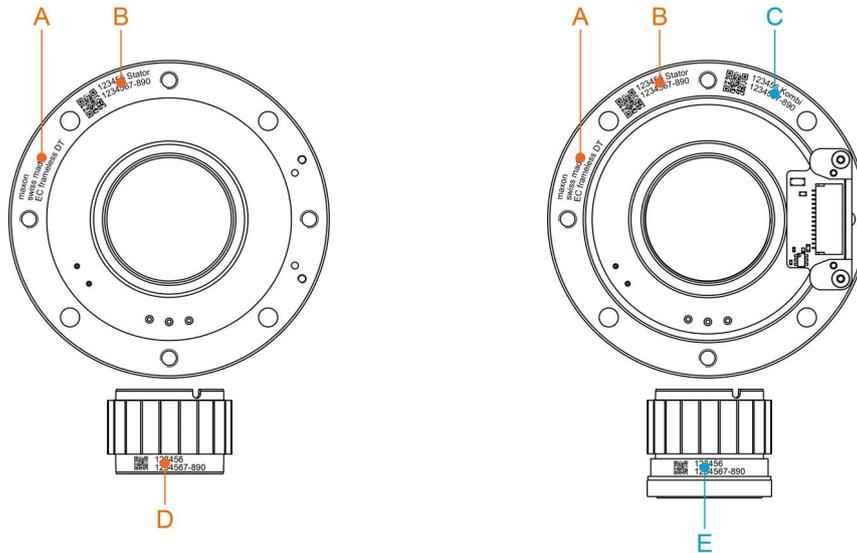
Typenschild (typisch) – EC frameless DT ohne (links) und mit TSX MAG Encoder (rechts)
